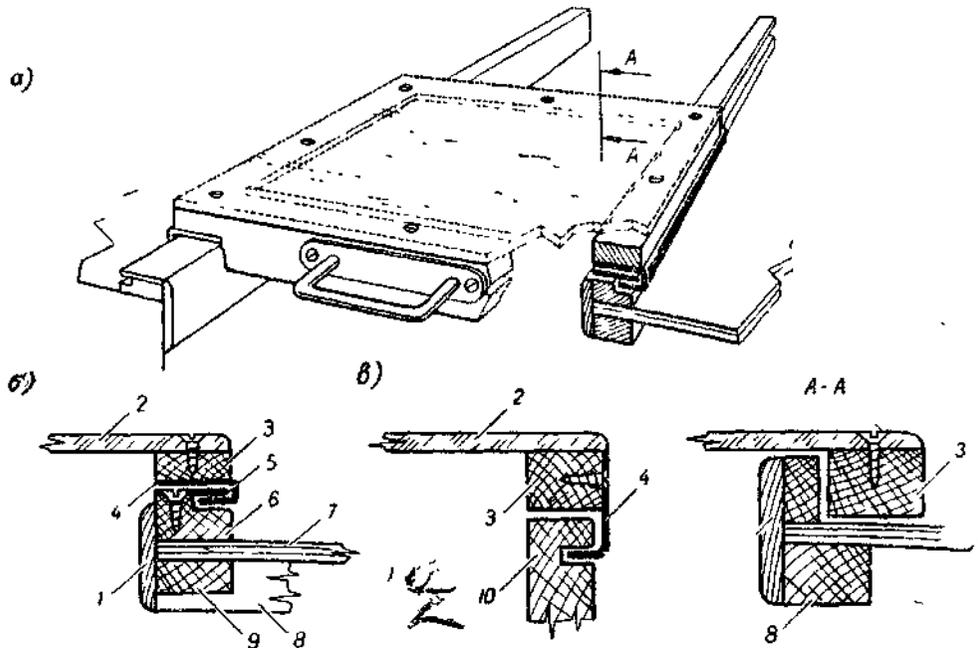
Сдвижной люк: а — общий вид; б, в — варианты скользящих люков.
